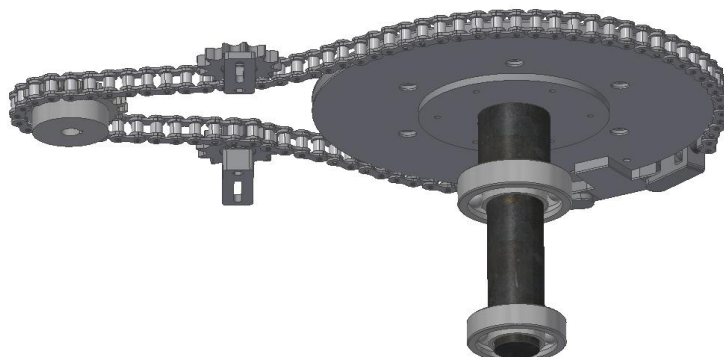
Pohled shora na otočný mechanismus stolu
